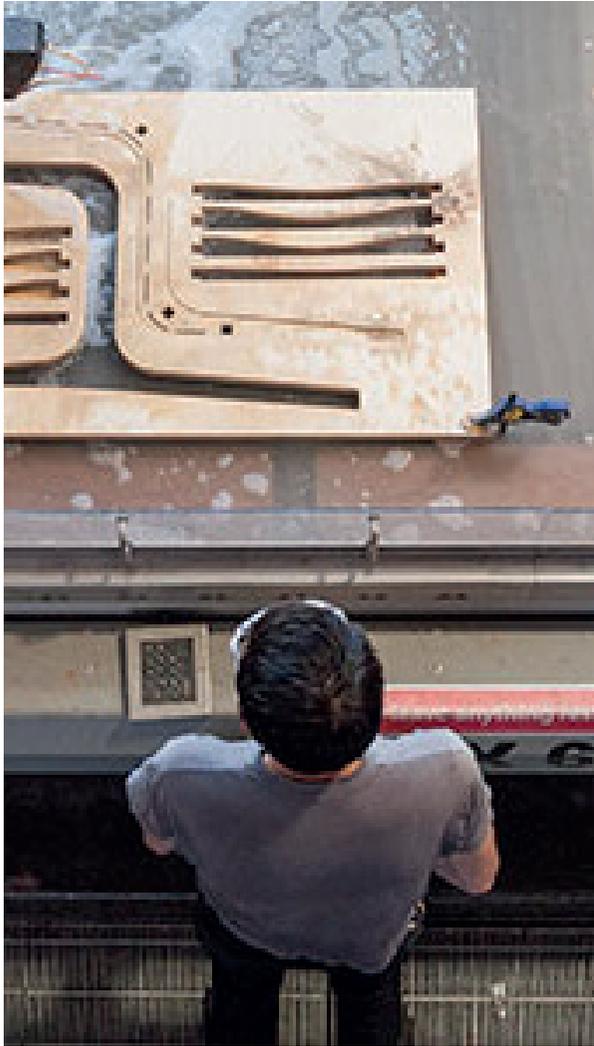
CAD/CAM Diseño y manufactura asistido por computador.
